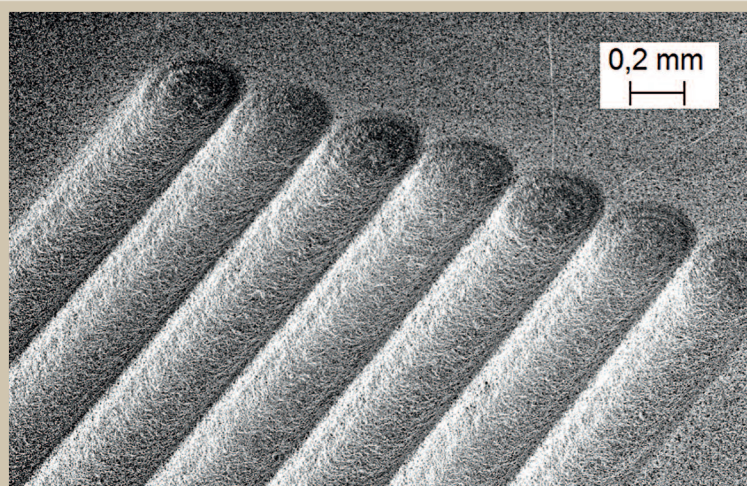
Jet-EC-bearbeiteter Bereich mit Mikrokanälen auf einer Werkstückoberfläche aus Hartmetall WC-Co6 [3]
